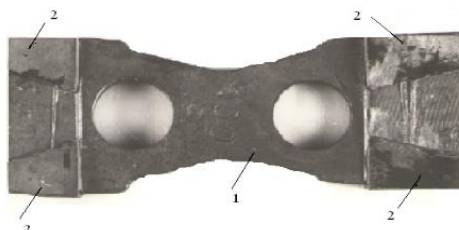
Конструкція молотка-модуля (основа 1-сталь Ст.3, сталь 45; 2-модульні пластини – вставки з порошкового композиційного матеріалу(КХЖ70, КХНФ15.); кормодробарка ДБ-5 (ДЗ-3), КДУ-2,0
